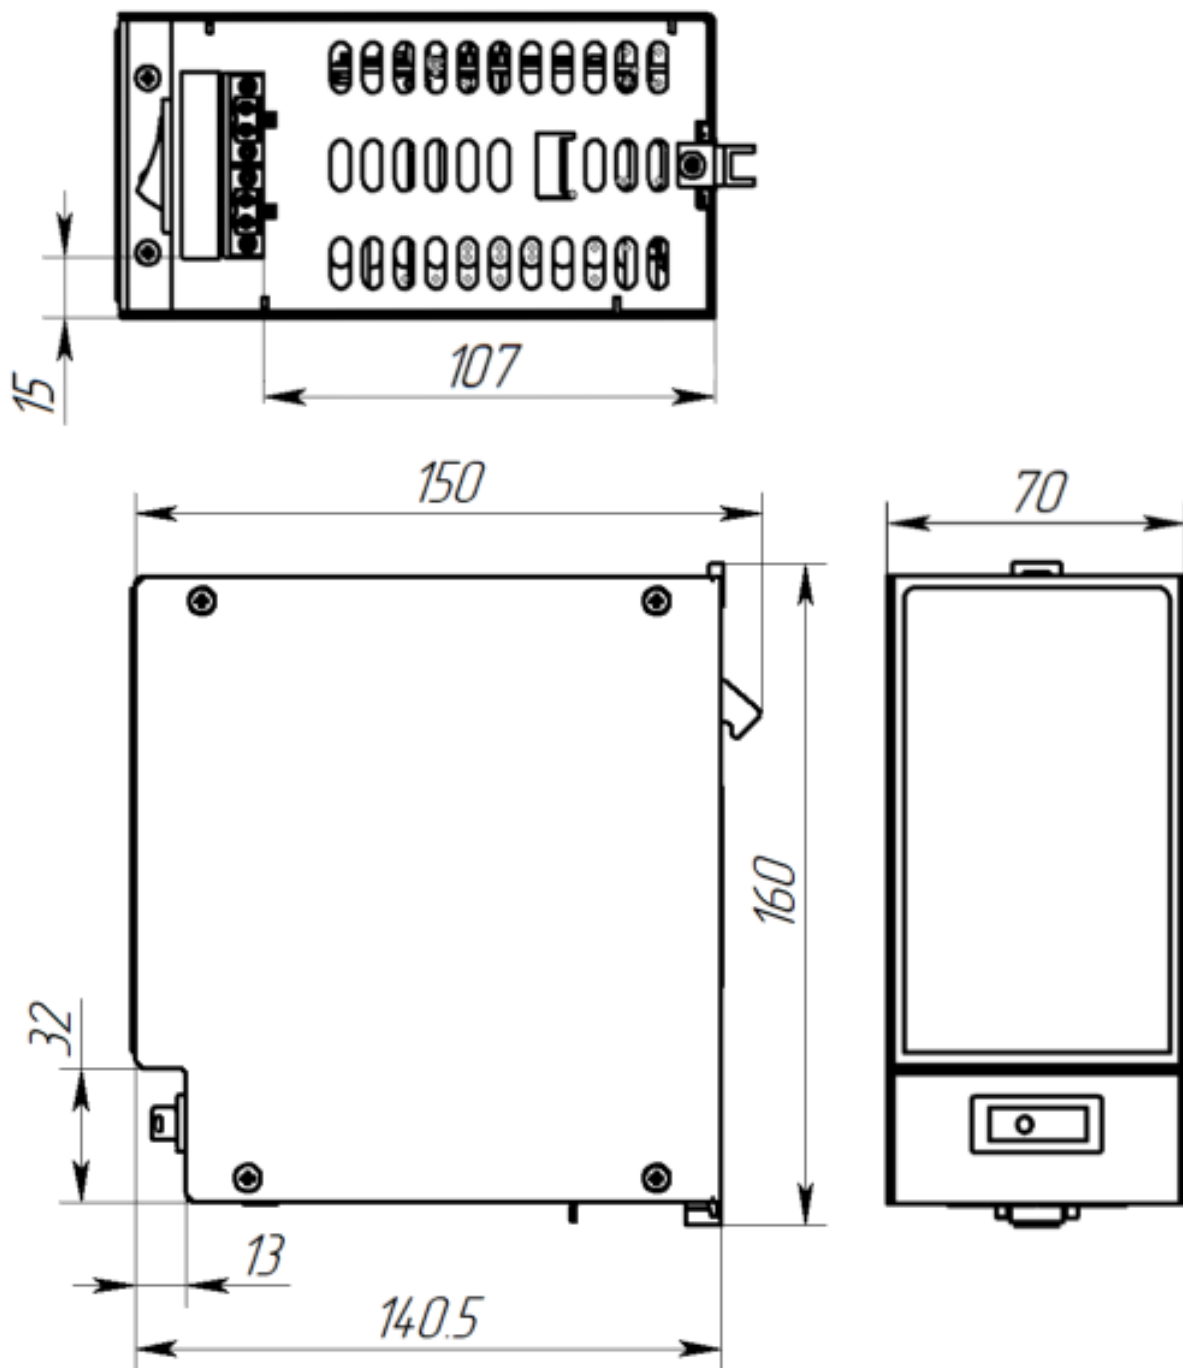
Габаритные и присоединительные размеры модуля питания в металлическом корпусе
